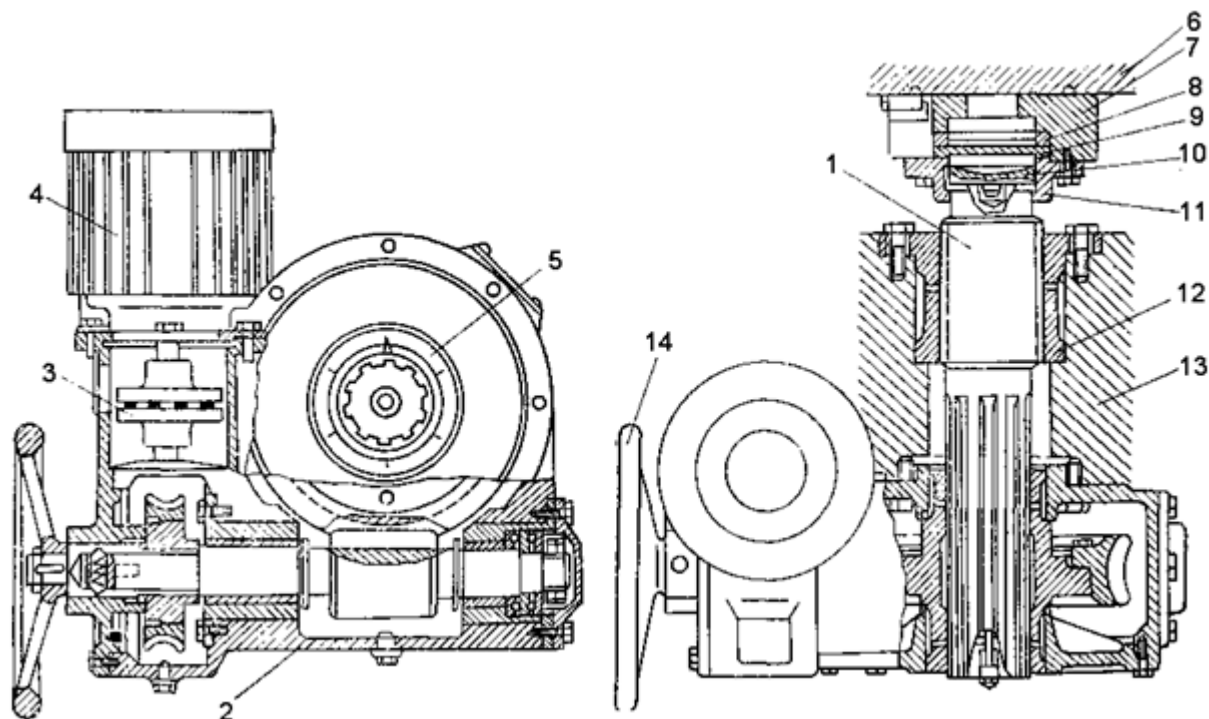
Механізм регулювання зазора: 1 – натискний гвинт; 2 – черв'ячний редуктор; 3 – еластична муфта; 4 – електродвигун; 5 – покажчик величини зазора; 6 – корпус підшипника валку; 7 – корпус запобіжного пристрою; 8 – матриця; 9 – запобіжна шайба; 10 – пуансон; 11 – кришка; 12 – гайка натискного гвинта; 13 – станина вальців; 14 – маховичок
